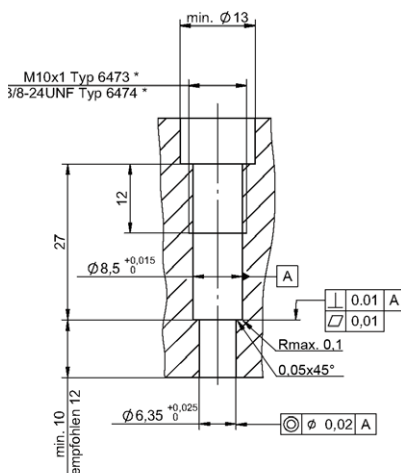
Bohrung für Direkteinbau mit Montagenippel
